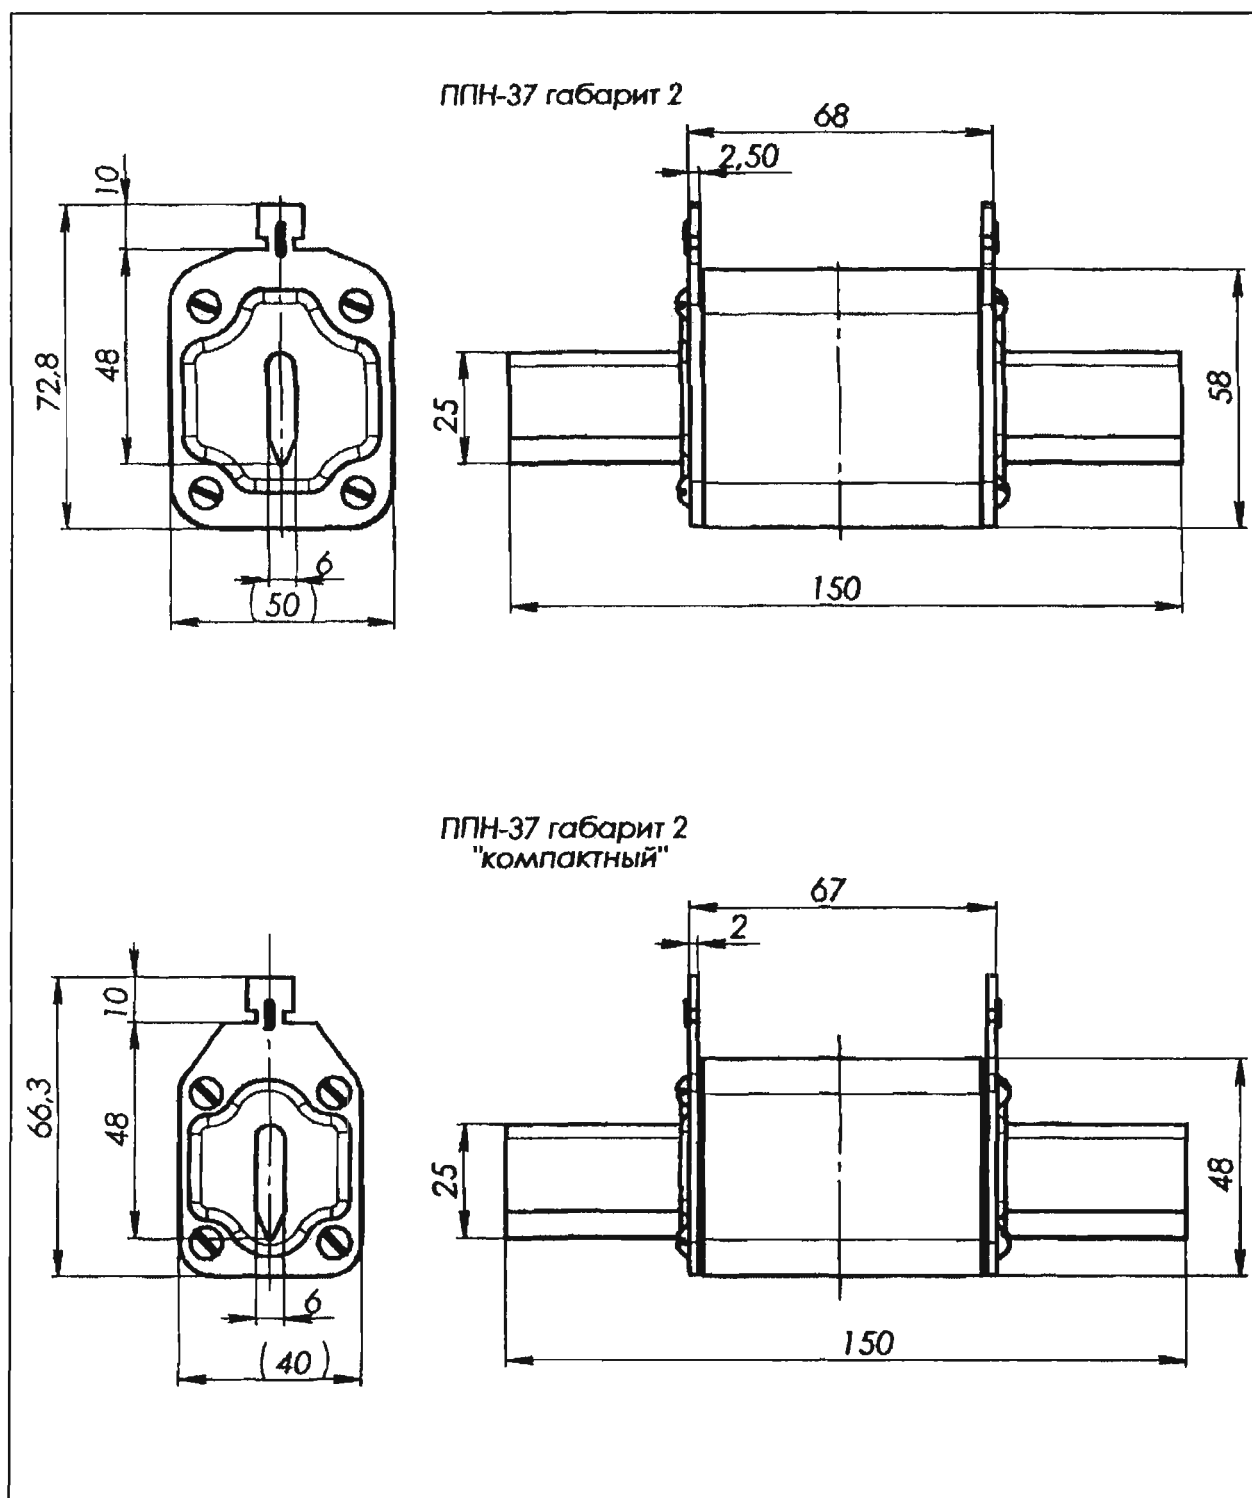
Габаритные и установочные размеры предохранителей серии ППН-37
